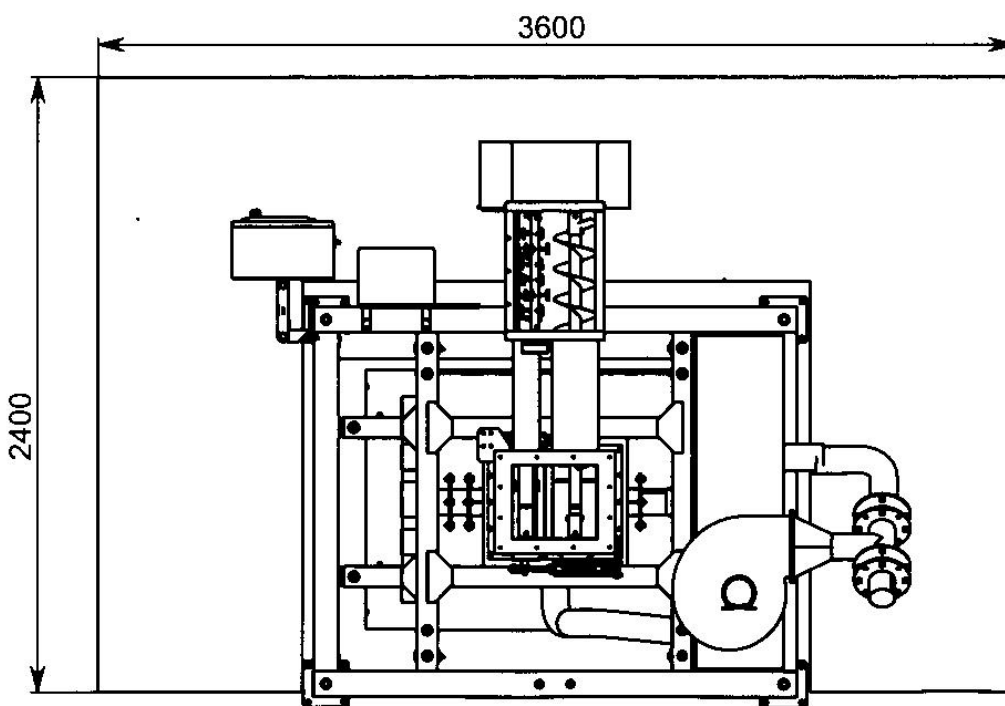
Габаритно-установочные размеры дозатора. Вид с верху.
